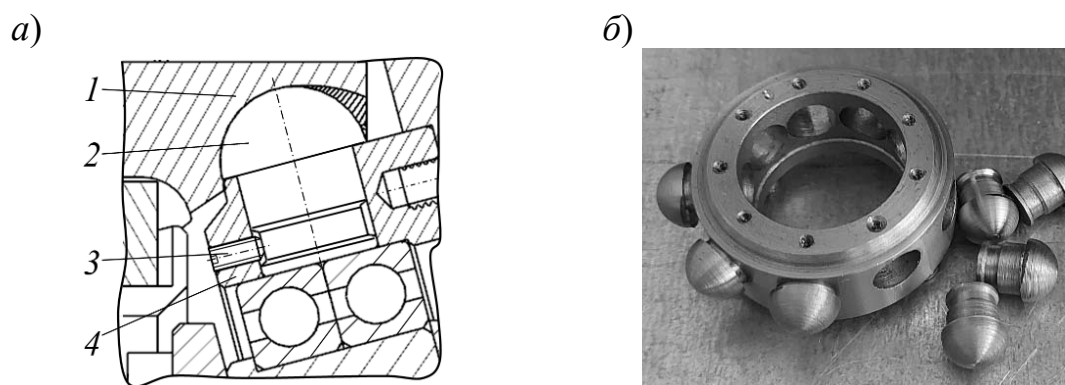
Механизм фиксации ролика: *а* – схема; *б* – детали образца
